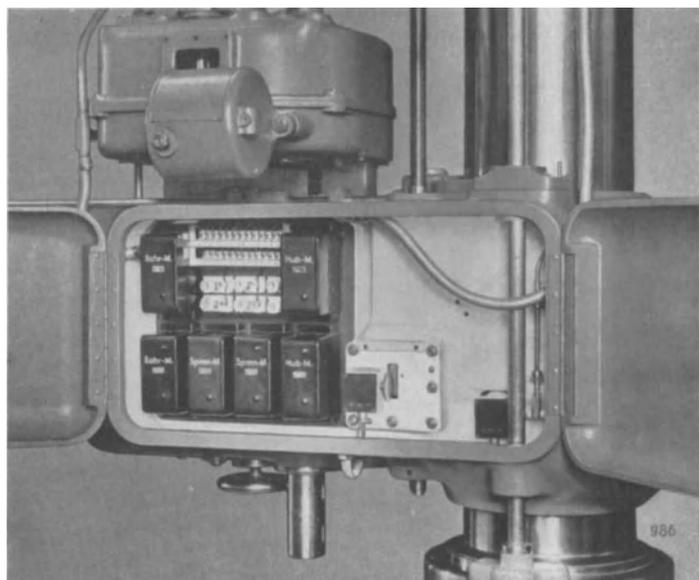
Apparateschrank im Ausleger einer Raboma-Radiale
